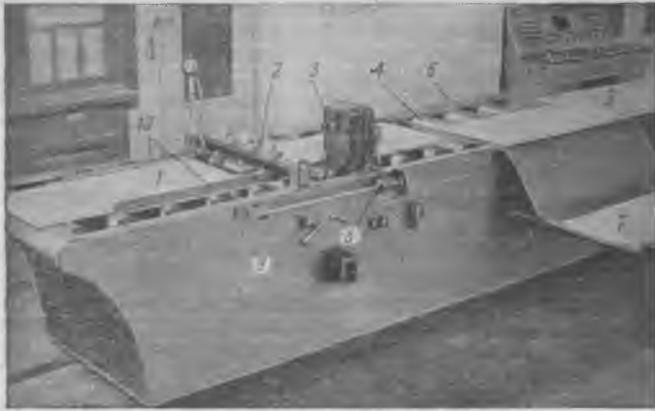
Общий вид автоматического контрольно-сортировочного устройства:
